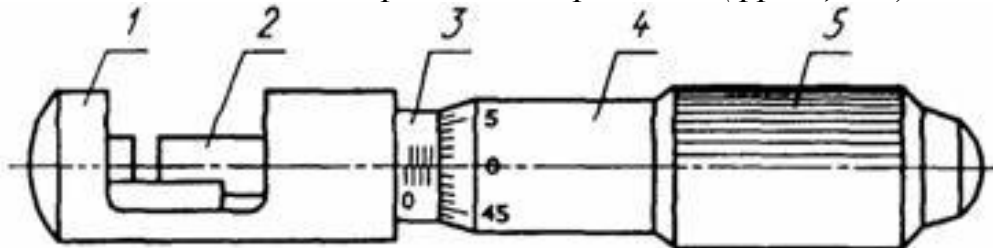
Тип МП. Мікрометрична головка: 1 - корпус; 2 - мікрометричний гвинт; 3 - стебло; 4 - барабан; 5 - тріскачка (фрикційна)
